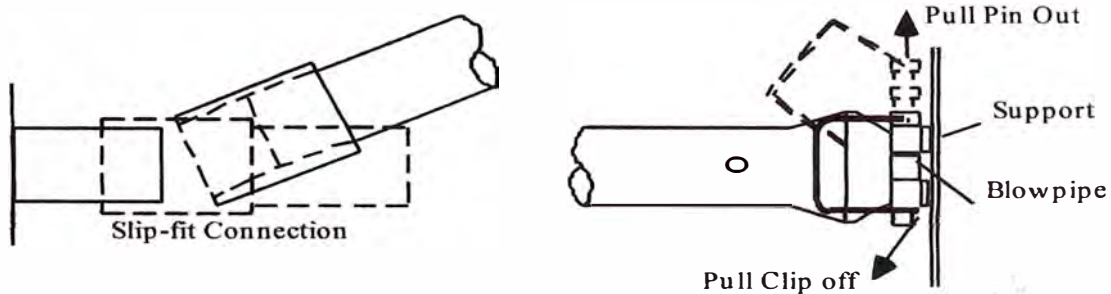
Montaje y desmontaje de flautas por deslizamiento
